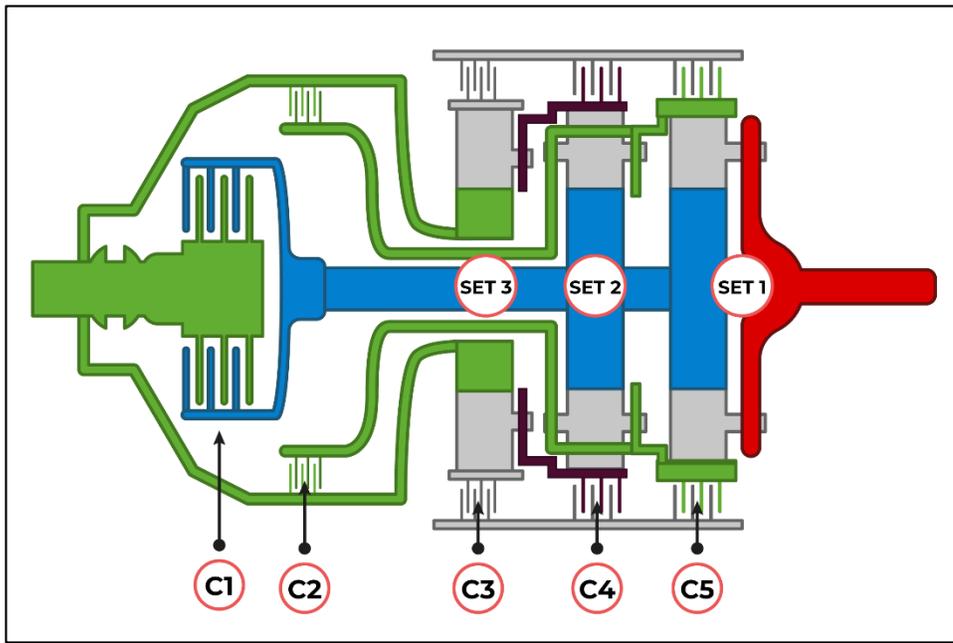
Sistema en dos dimensiones de engranajes planetarios
